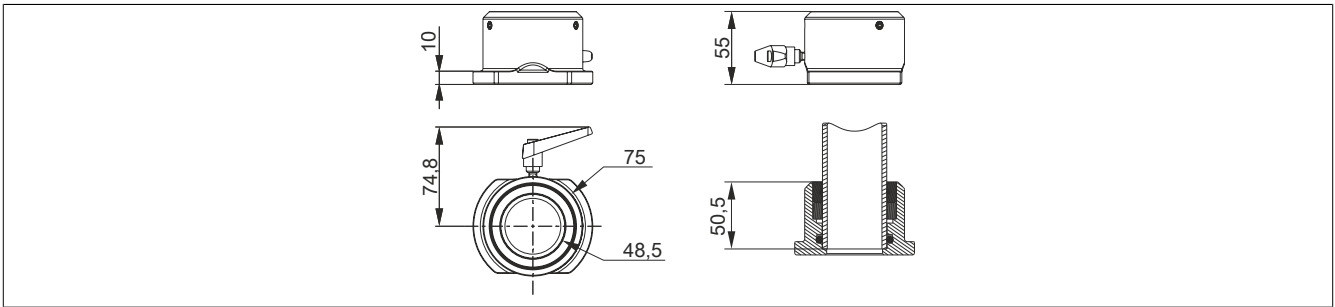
5ACCFL00.0000-000 - Abmessungen
